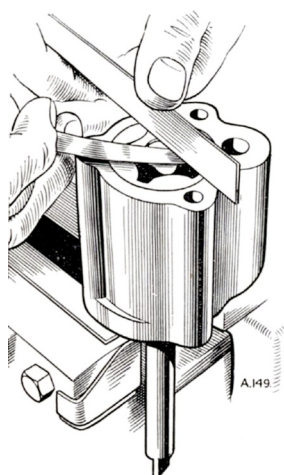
Mesure du jeu en bout des rotors de la pompe à huile
